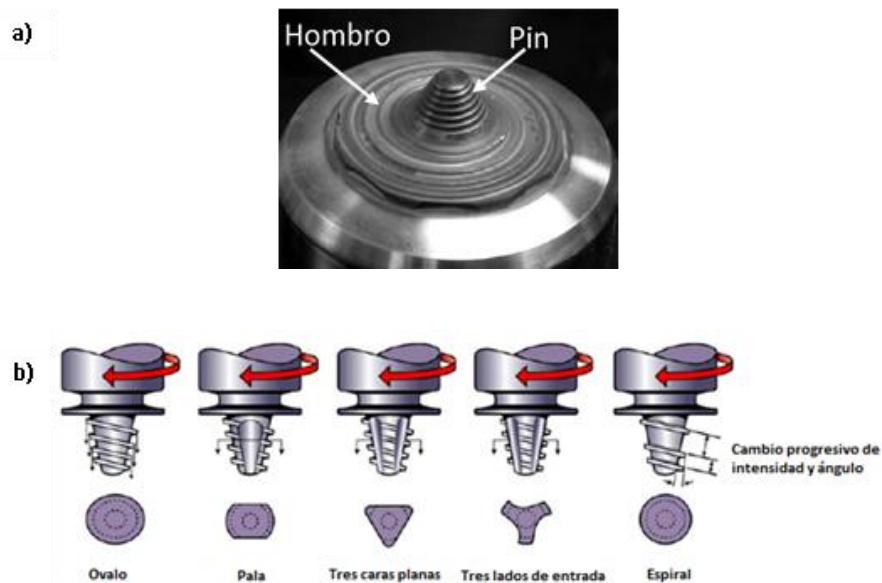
(a) Esquema de las partes principales herramienta para proceso FSW (b) geometrías básicas de la herramienta para soldadura FSW.
